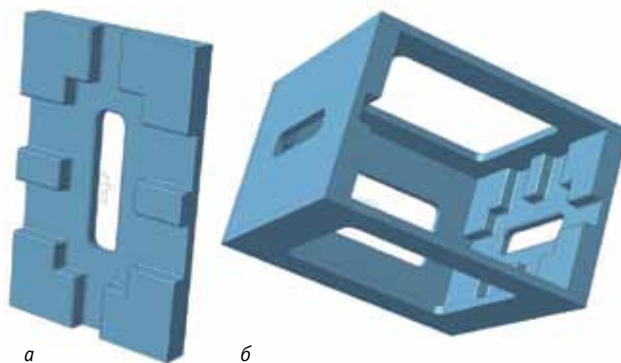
Типовые элементы станины горизонтально-расточного станка модели 2620: а – типовой элемент, б – сборочный модуль
